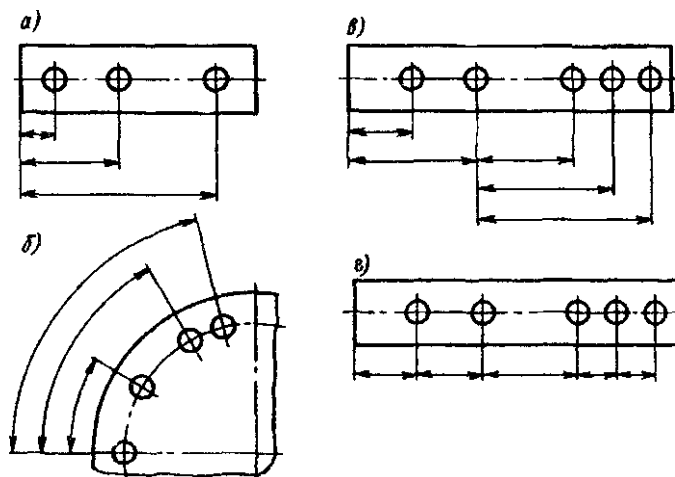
Нанесение размеров: а, б — от общей базы; в — от нескольких общих баз; г — цепочкой
